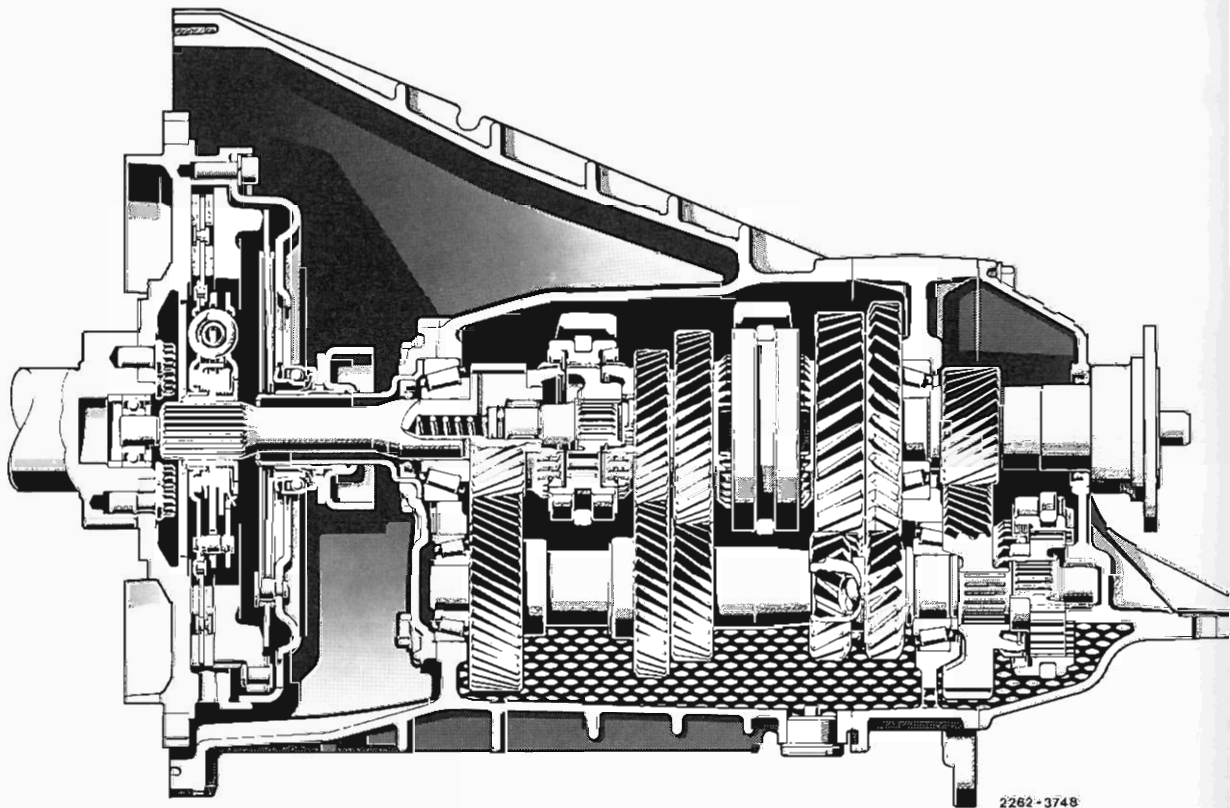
/1 5-Gang-Schaltgetriebe 717.436 (GL 76/27-5) Typen 460.317/328/329/337/338
